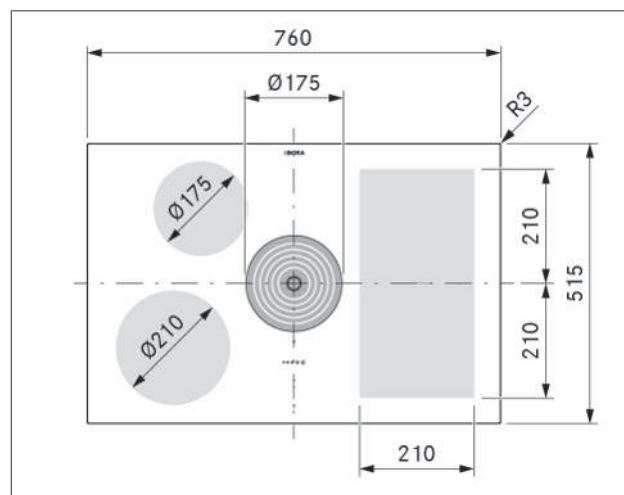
Dimensioni apparecchio vista dall'alto
